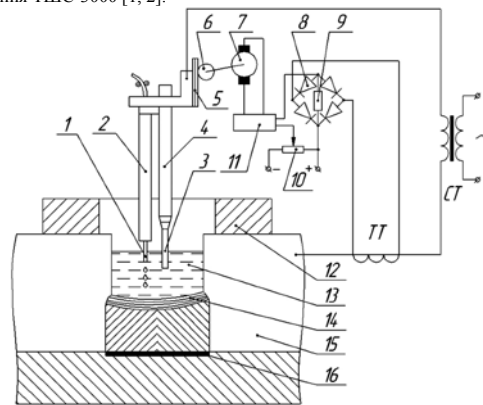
Схема сварки комбинированным электродом: 1 – проволока; 2 – направляющий канал; 3 – неплавящийся электрод; 4 – мундштук; 5 – рейка; 6 – зубчатое колесо; 7 – электродвигатель; 8 – выпрямитель; 9 – сопротивление; 10 – потенциометр; 11 – усилитель; 12 – формирующая накладка; 13 – шлаковая ванна; 14 – металлическая ванна; 15 – свариваемые кромки; 16 – заправка
